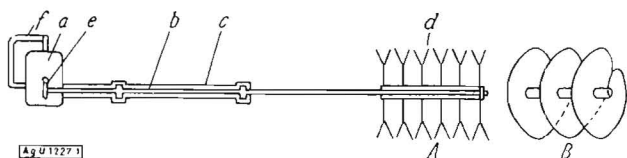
Schema der Elektrofräse mit Schaufel- und Messerfräser sowie Schema des Schraubenfräses
